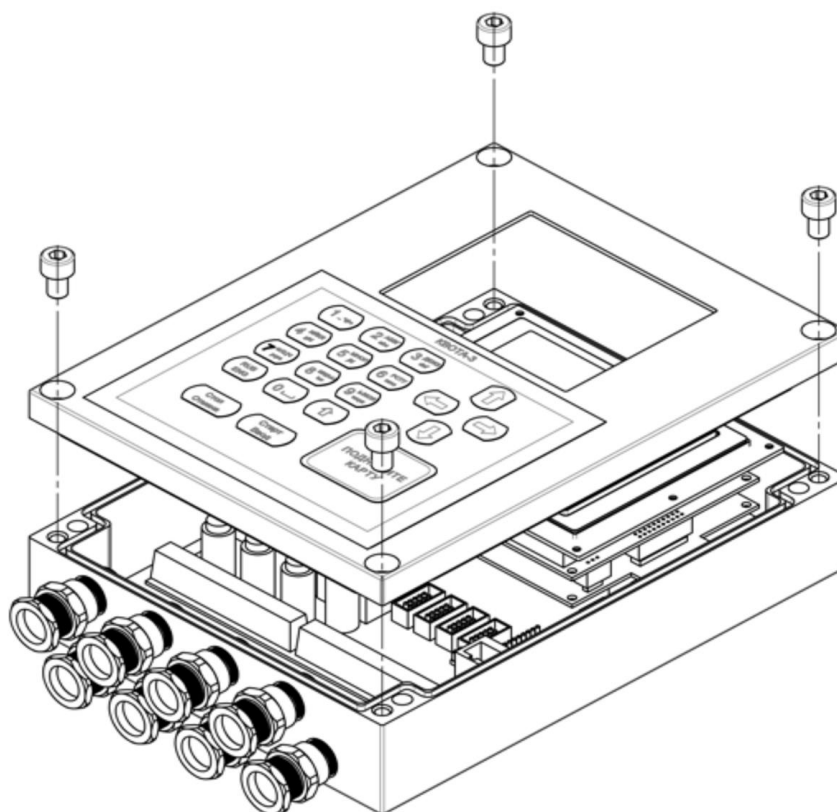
Снятие крышки корпуса контроллера «Квота-3»
